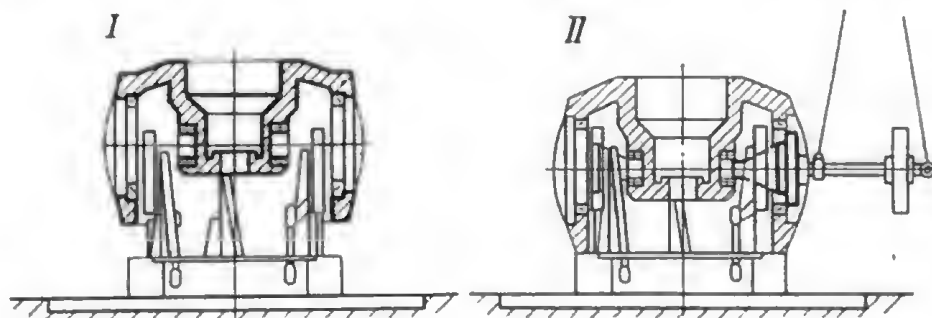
Схема сборки рычагов, серг и цапф без кантовки втулки.
